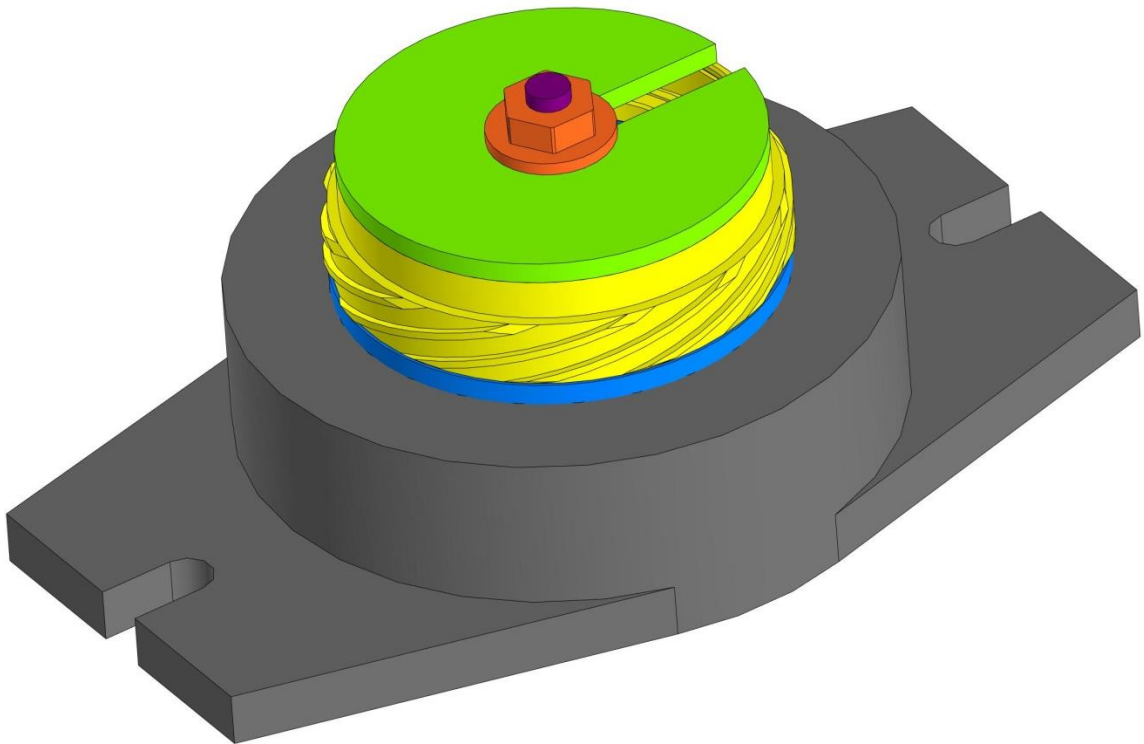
Спроектований верстатний пристрій та закріплена деталь
